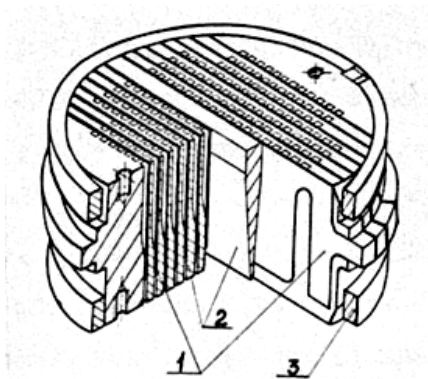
Конструкция прямооточного клапана типа ПИК: 1 – седло; 2 – пластина; 3 – кольцо
